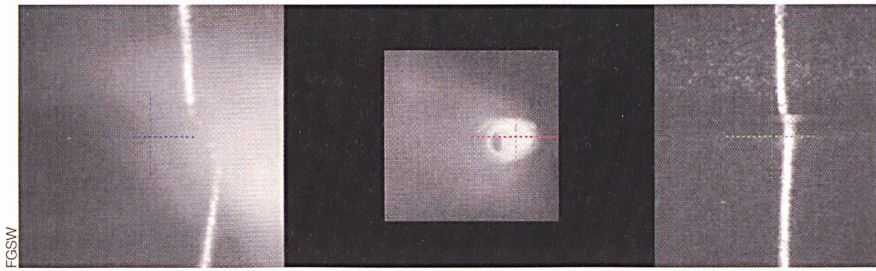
Simultane Bildaufzeichnung beim Laserschweißen.
